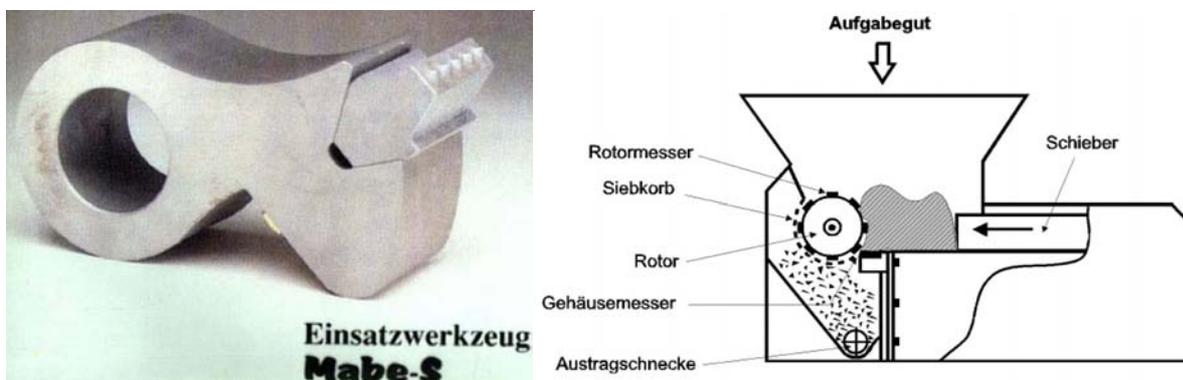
Werkzeug des Schlegelhäckslers und Einwellenzerkleinerer
